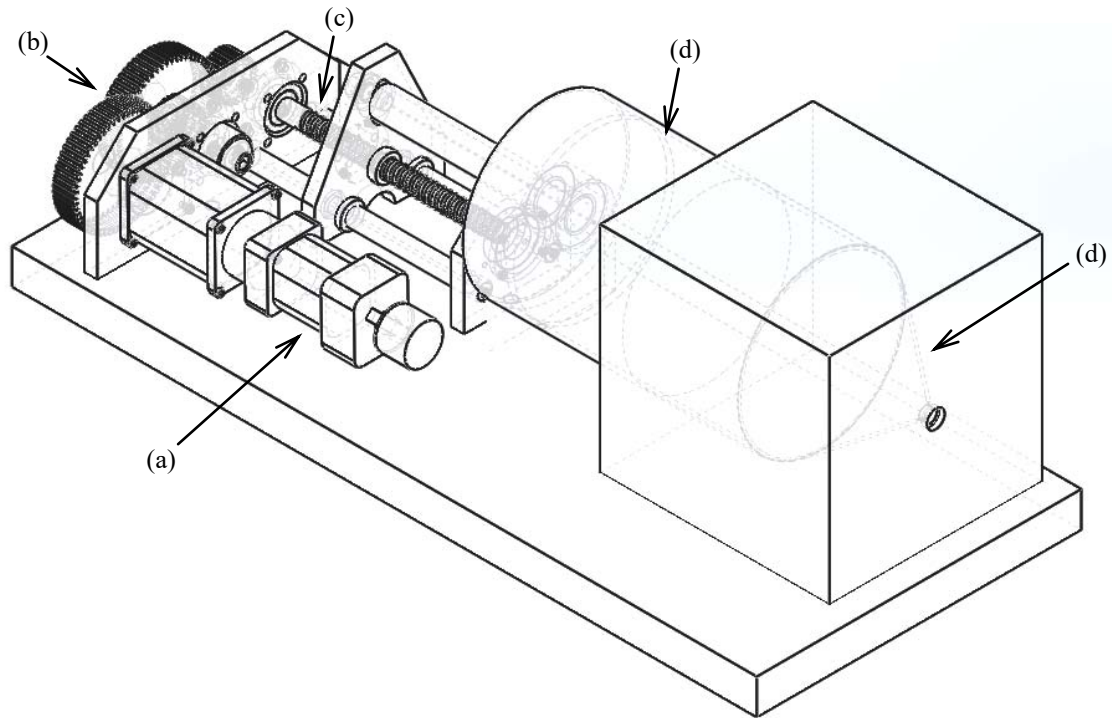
Dispositivo de bombeo conformado por: (a) servo motor, (b) tren de engranes, (c) tornillo de bolas, (d) sistema cilindro-pistón y (e) boquilla.
